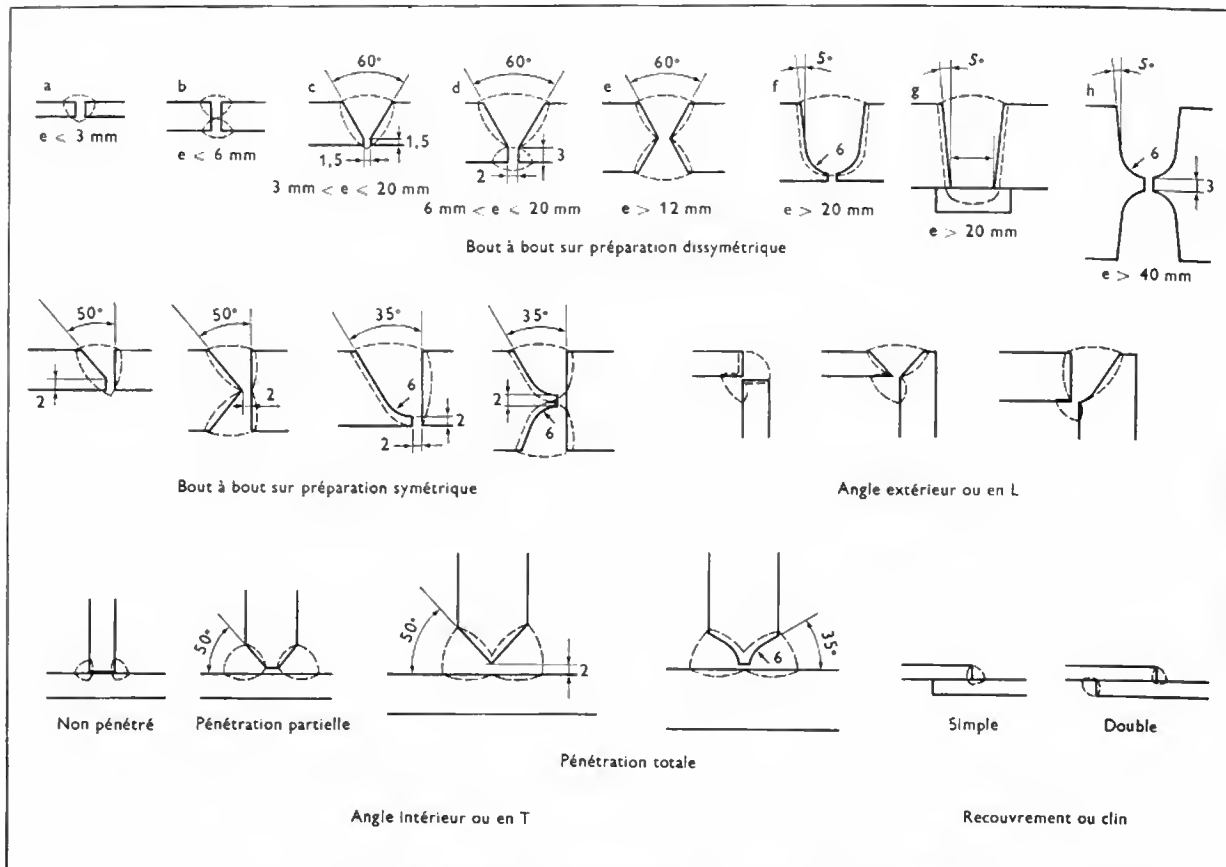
Préparations et formes de soudures à l'arc avec électrodes enrobées
